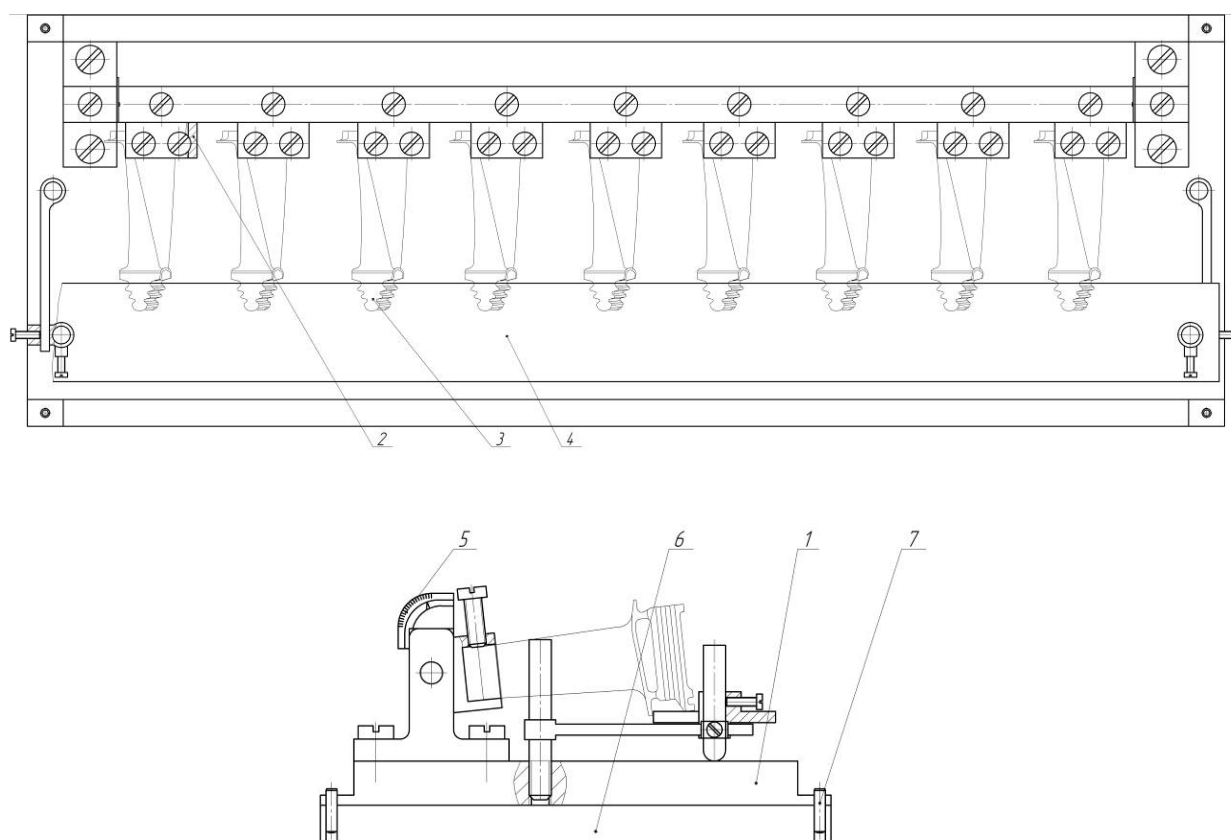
Схема касетного приспособлення: 1 – плита; 2 – установочний елемент; 3 – деталь; 4 – підйомна планка; 5 – кутомір; 6 – поворотна плита; 7 – штифт
